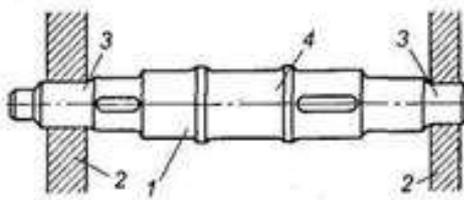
Прямой вал: 1—вал; 2—опоры вала; 3—цапфы; 4—шейка
